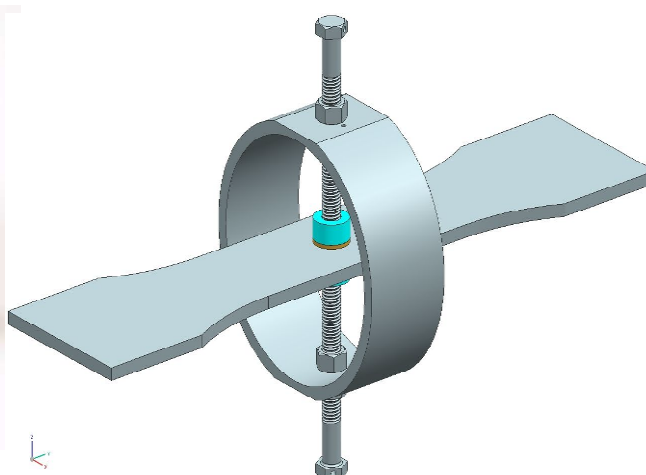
Трехмерная модель образца и приспособления для получения прижимных усилий
